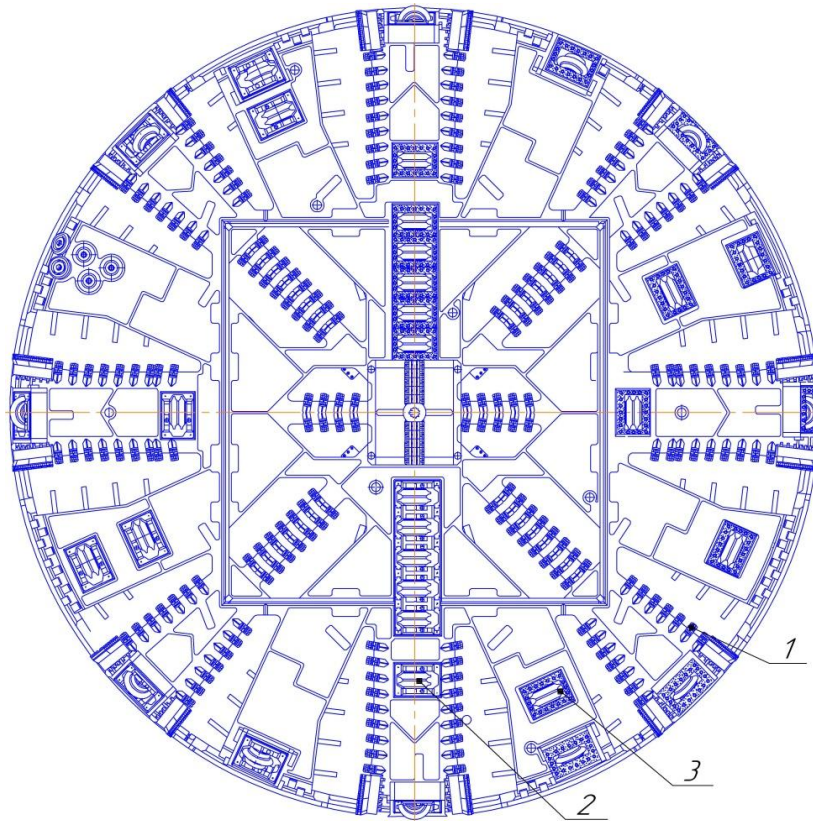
Роторный исполнительный орган ТПМК Herrenknecht S-782
